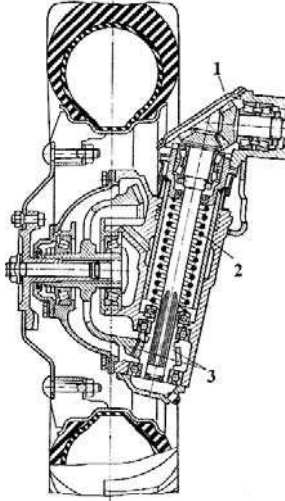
Передній міст з підресореними направляючими колесами (крутний момент підводиться без з'єднувальних муфт): 1, 3 - дві пари конічних шестерень; 2 - циліндрична пружина
